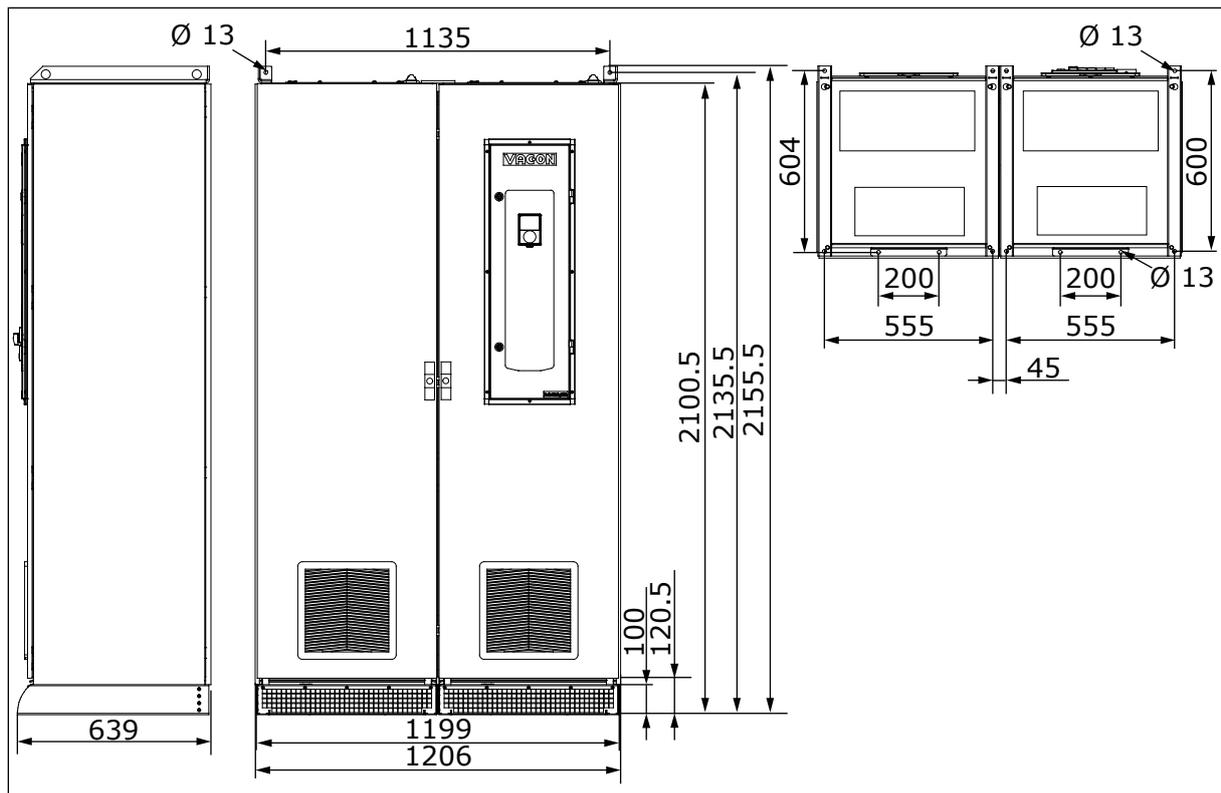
Abmessungen des Standard-Schaltschranks in mm, MR11 und MR12, IEC
